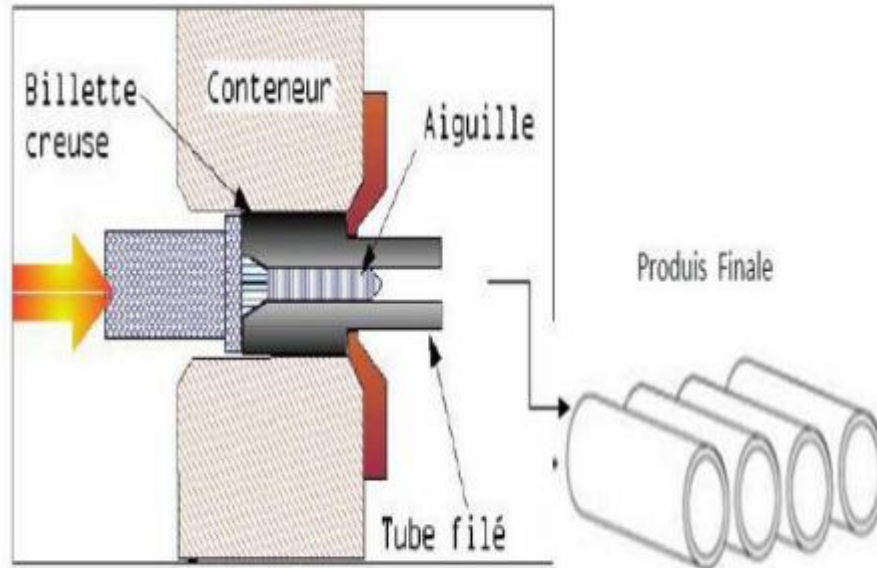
Fabrication de pipelines sans soudure
